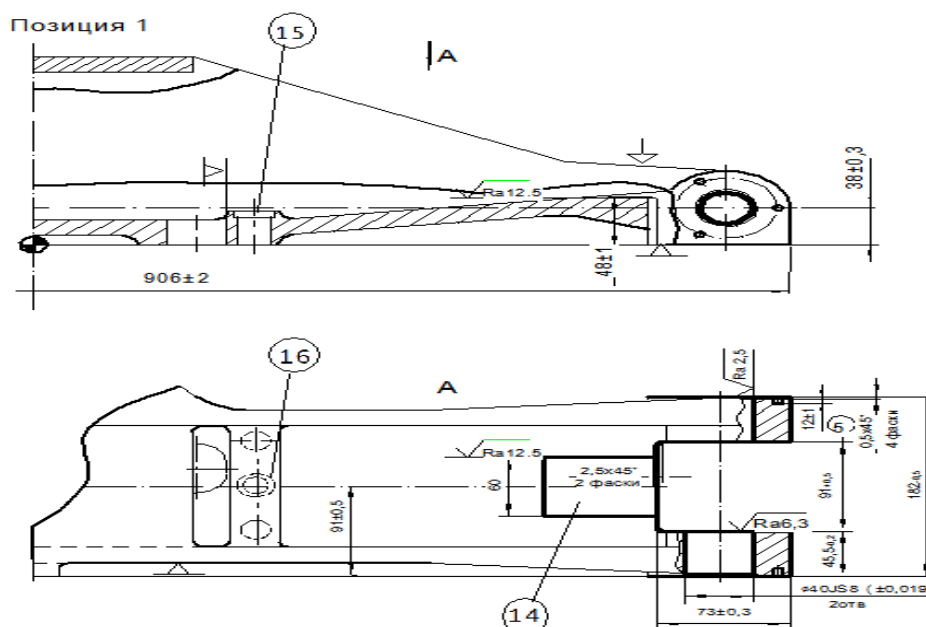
Чертеж детали. Поверхности подлежащие обработке на втором установе
